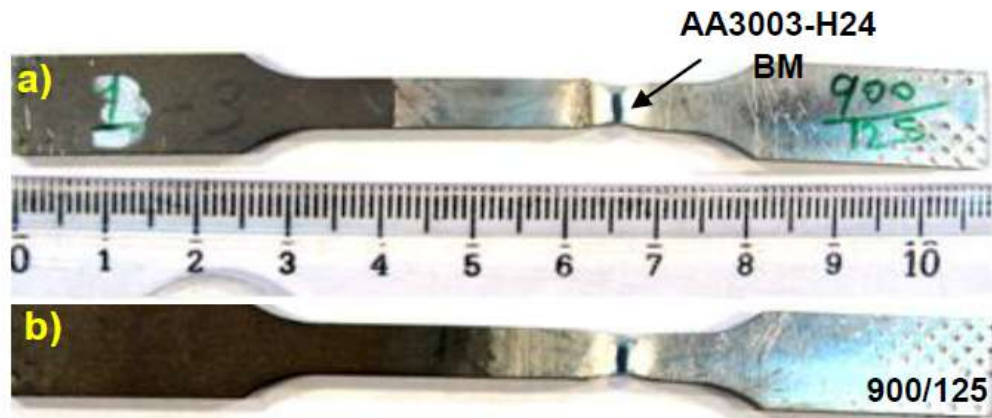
Probetas del ensayo de tensión después de la soldadura por fricción bajo los parámetros de 900/125; a) parte superior y b) parte trasera ⁽³³⁾
